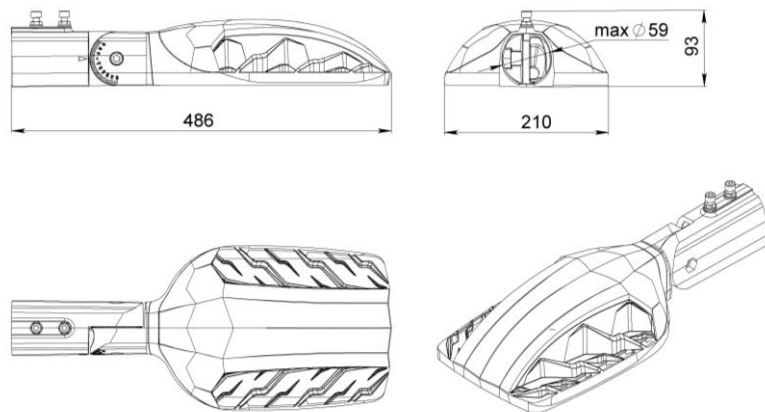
Общий вид светильника Street X1 с консольным поворотным креплением.
